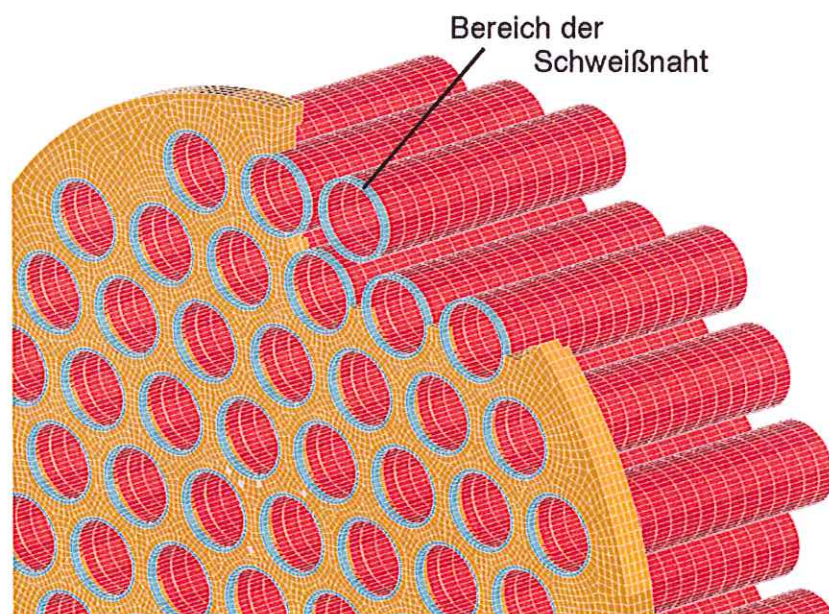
Ausschnitt aus dem dreidimensionalen Modellbereich. Mechanische Berücksichtigung der Schweißnähte, einige Elemente der Randzone zur Veranschaulichung ausgeblendet.
